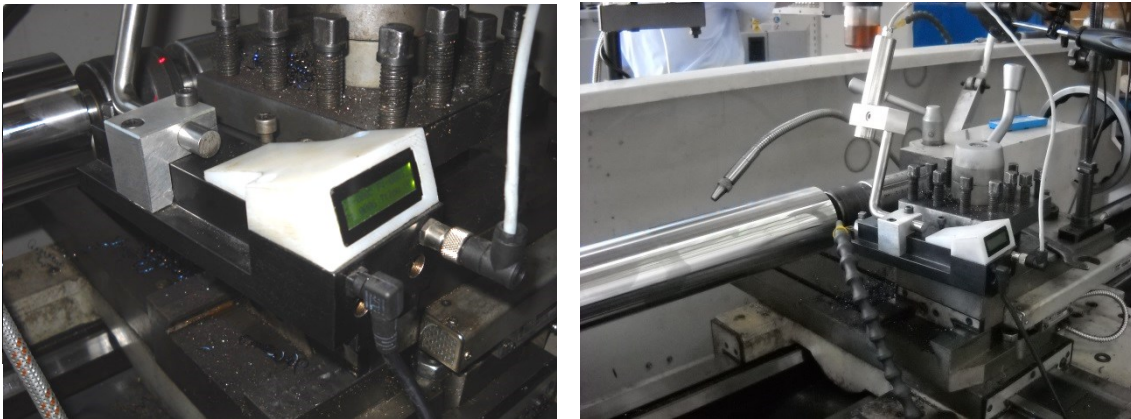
Măsurarea forțelor de așchiere la strunjire
